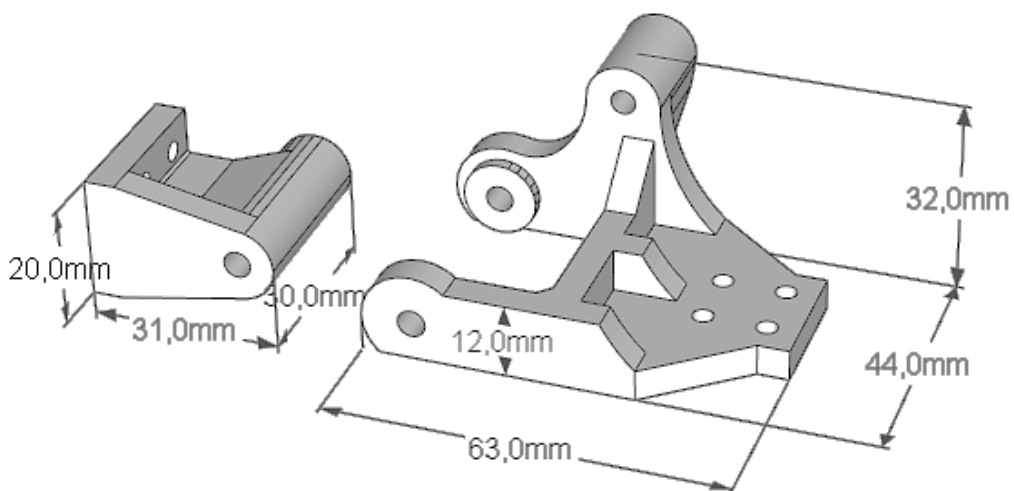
Конструкція шарнірного з'єднання в області встановлення захватного механізму
